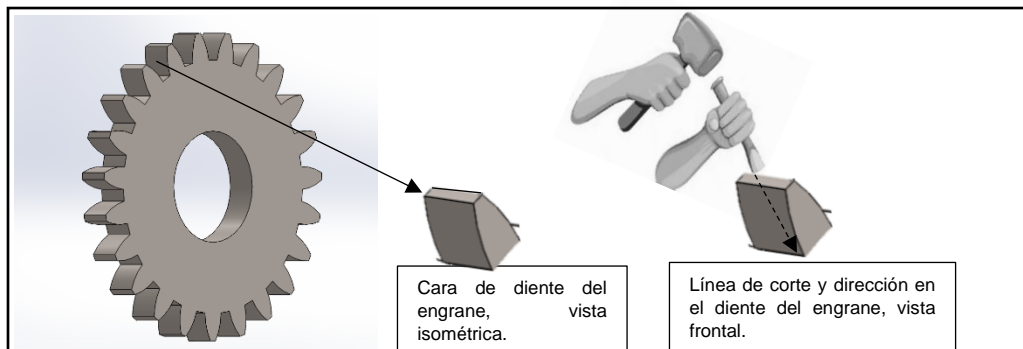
Planteamiento de la fractura artificial del diente del engrane.
